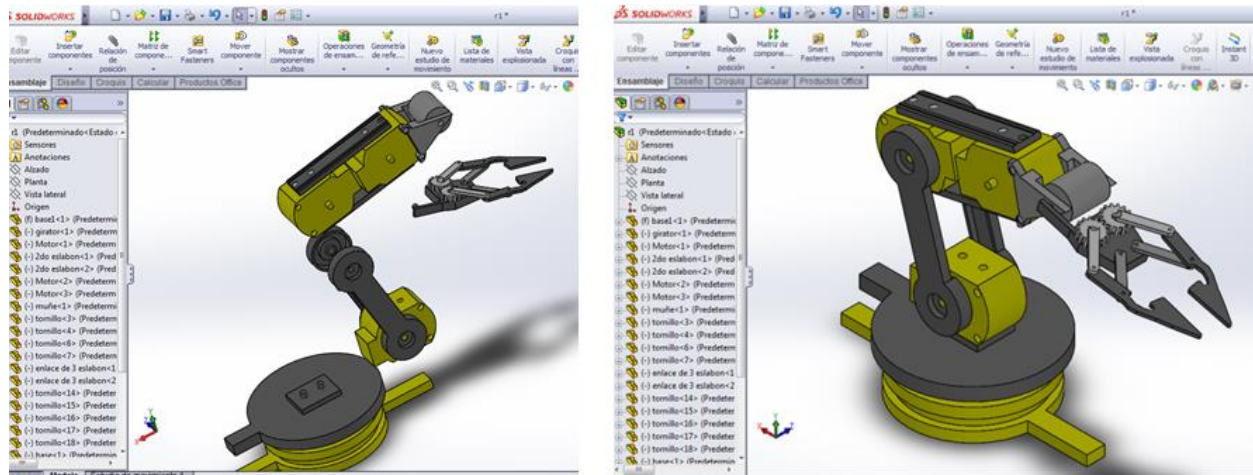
Izquierda: Piezas sin ensamblar, Derecha Robot ensamblado
